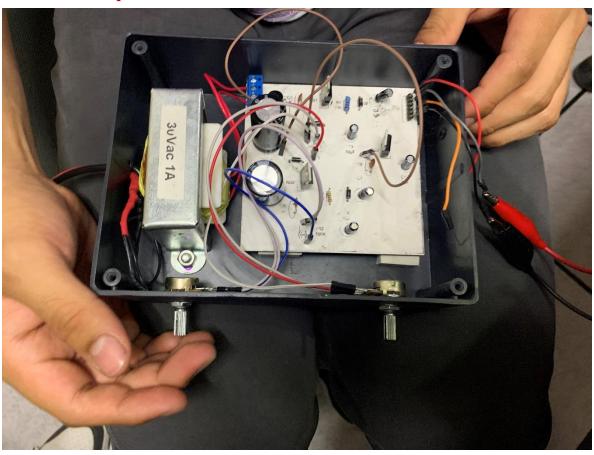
Diseño final de la fuente en PCB. Fuente: Elaboración propia
